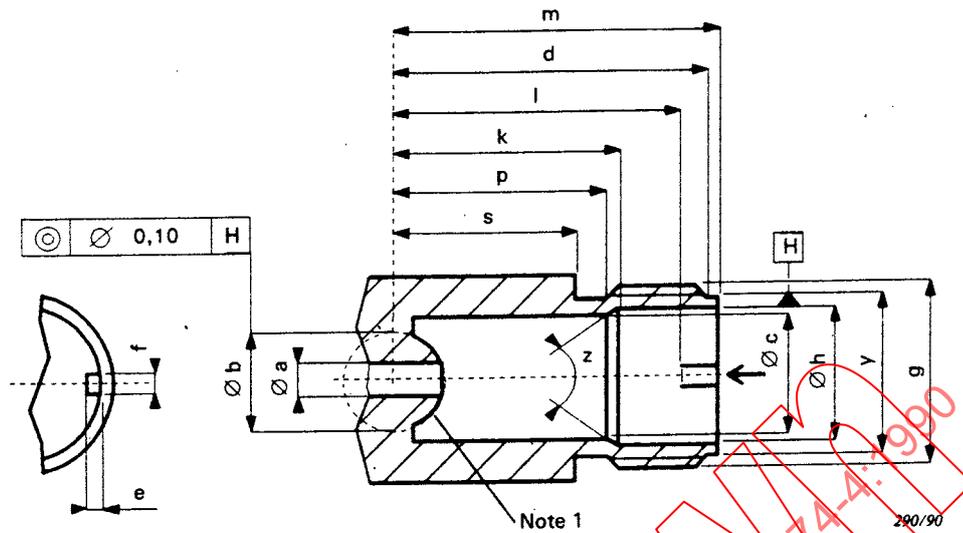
Dessin d'interface du raccord (pour les dimensions et la note, voir tableau 2)
